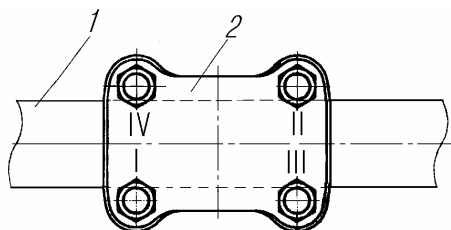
Схема затяжки гаек стремянок рессор: 1-рессора; 2-балансир задней рессоры (балка переднего моста); I-IV-порядок затяжки гаек стремянок
